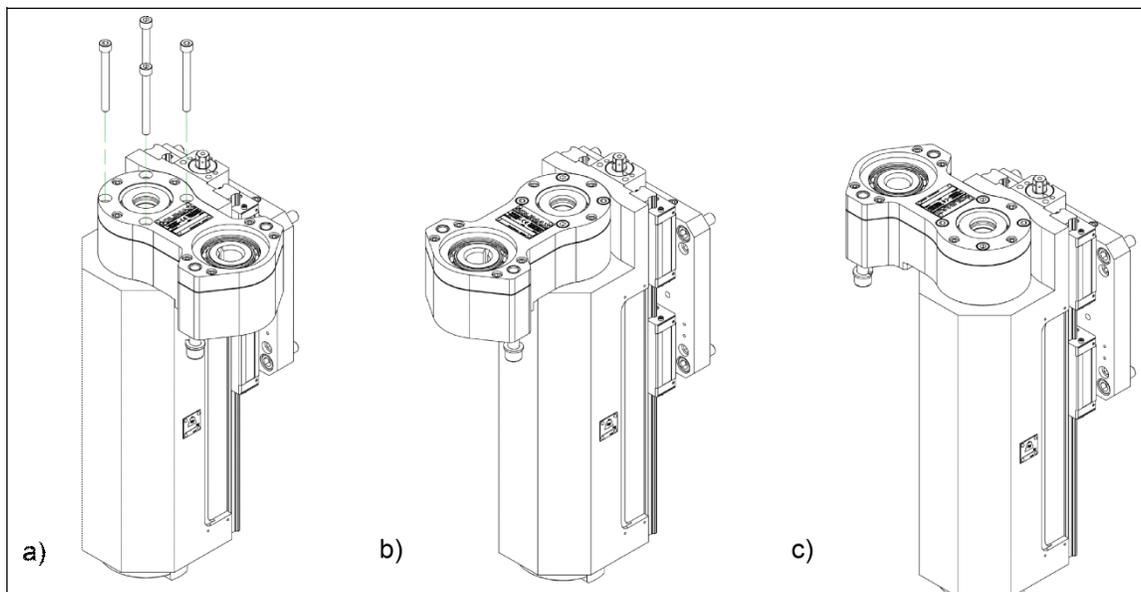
ROTACIÓN DE LA CAJA DE ENGRANAJES
